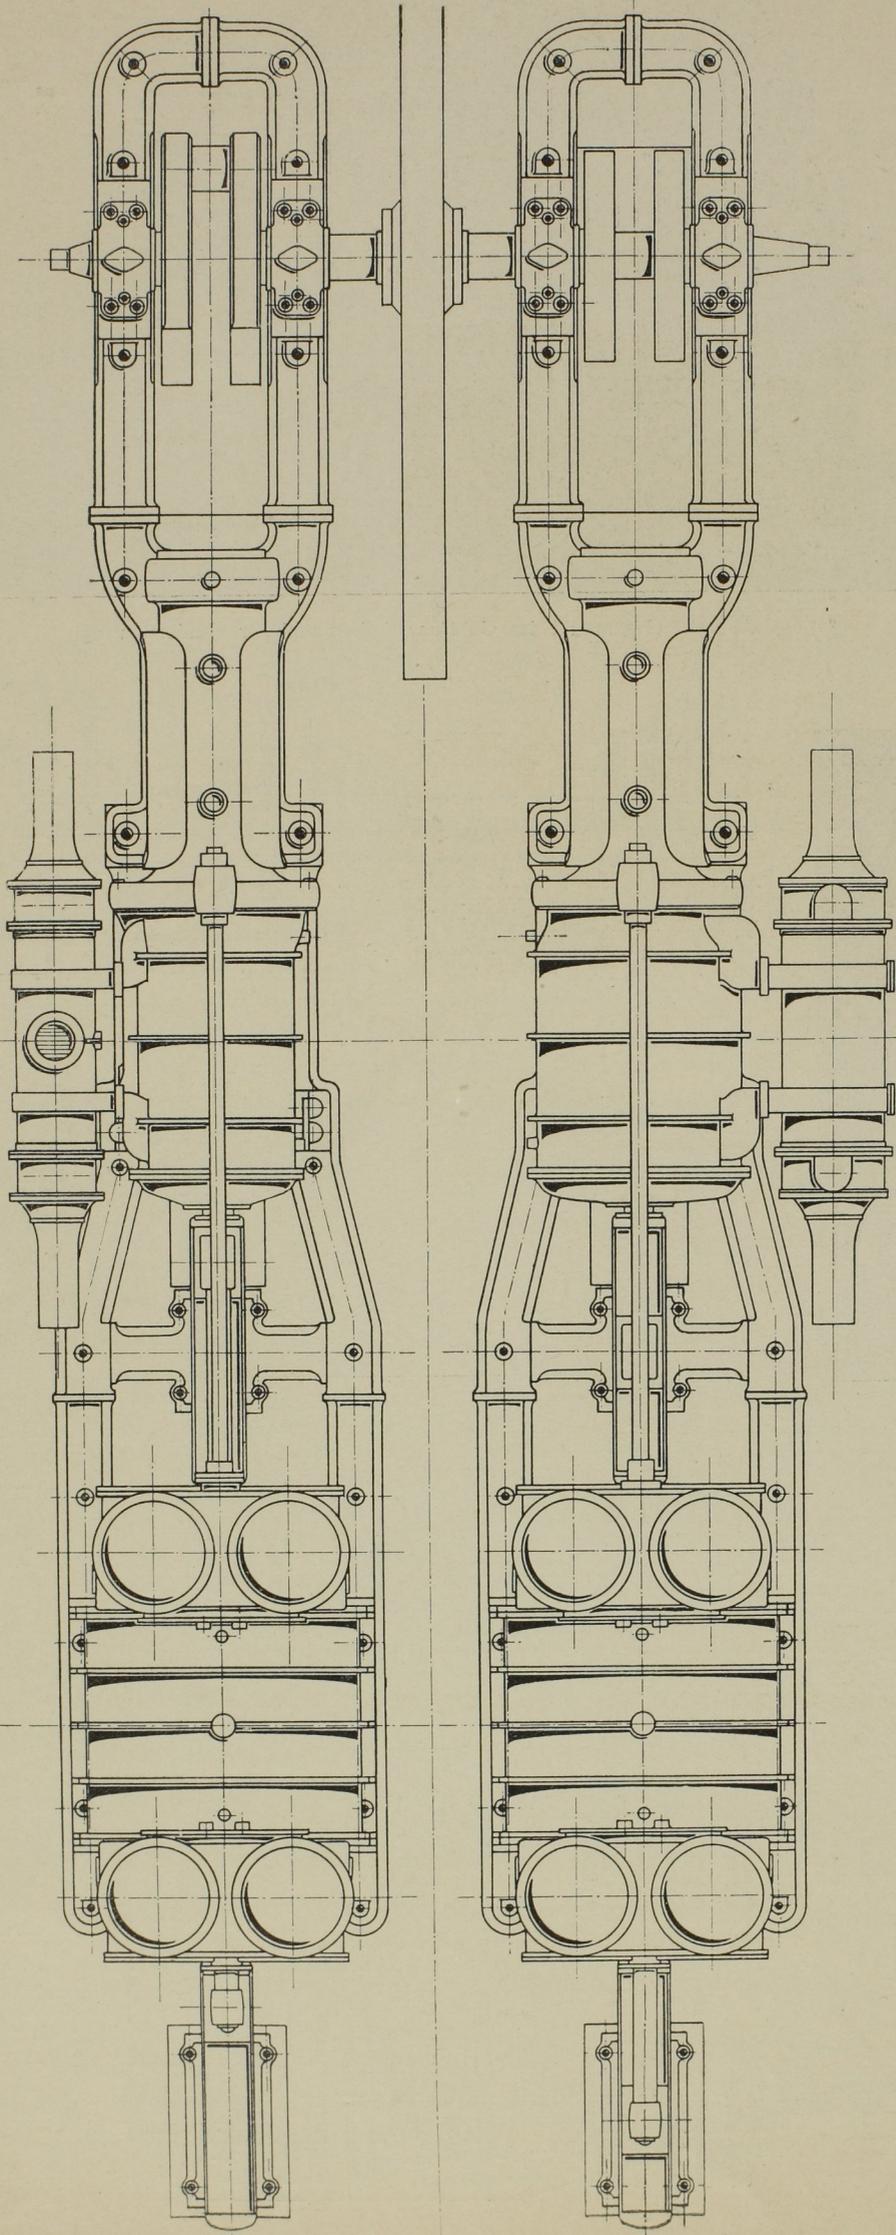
Grundriss der Gebläsemaschine. Massst. 1:60.
